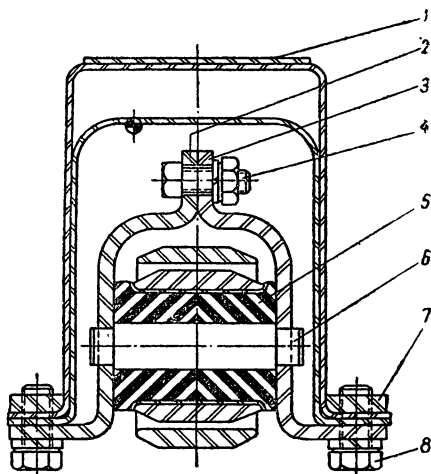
Крепление заднего конца задней рессоры автомобиля М-72:
